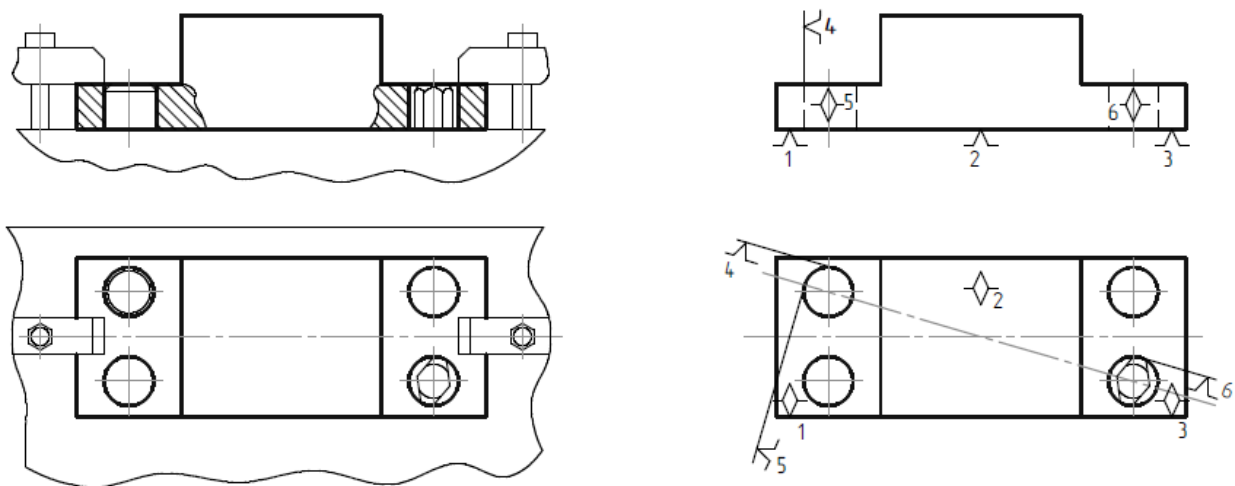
Базування корпусної заготовки на площину і два отвори
